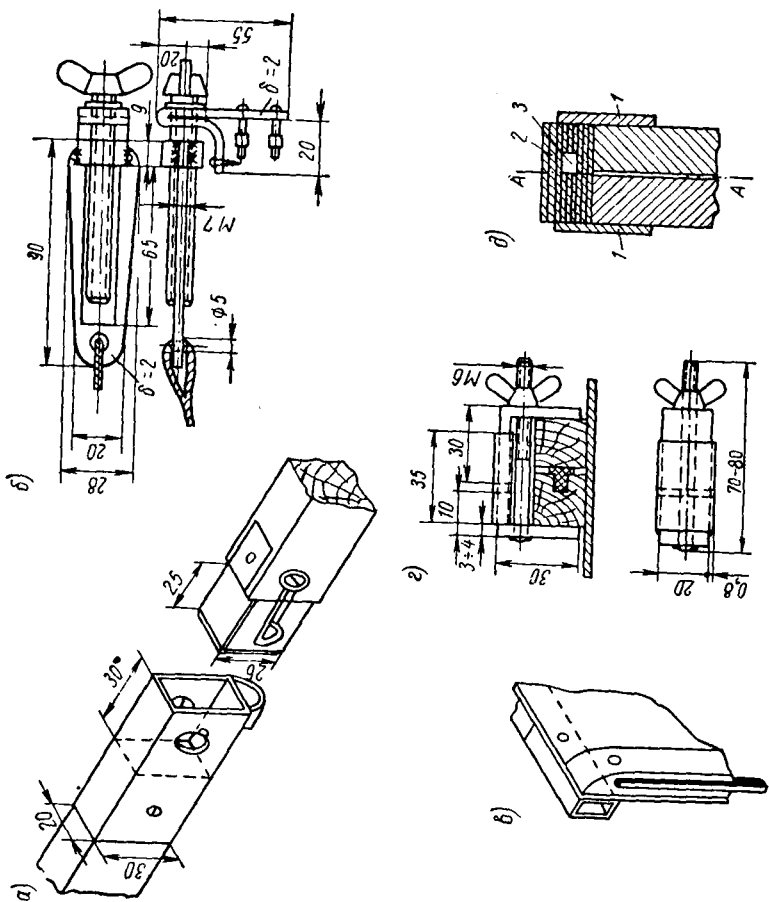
«Ладога» M2-A: а — шиповое соединение наружных привальных брусьев; б — натяжные приспособления (галереи) — два по бортам и один в кормовой части днища; в — резиновое уплотнение на 3 и 5-м шпангоутах; г — струбоцины для крепления шпангоутов; д — сечение стенок кондуктора со клееными из фанеры шпангоутами с пазом (А—А—линия распила).
